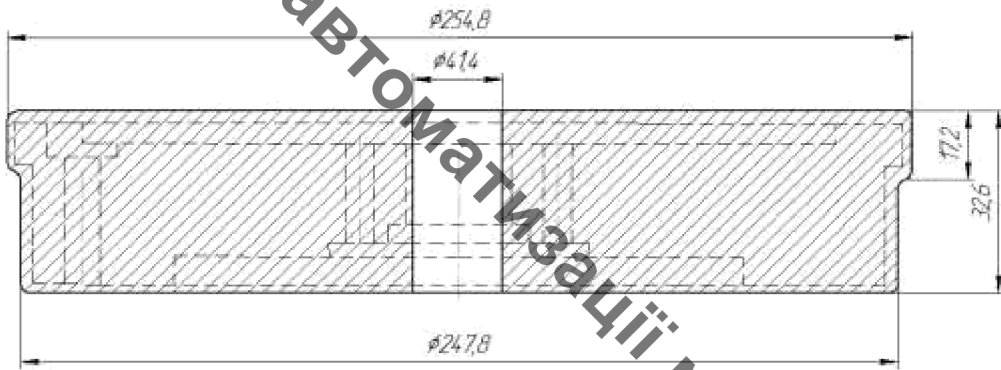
Ескіз заготовки в оболонковій формі
